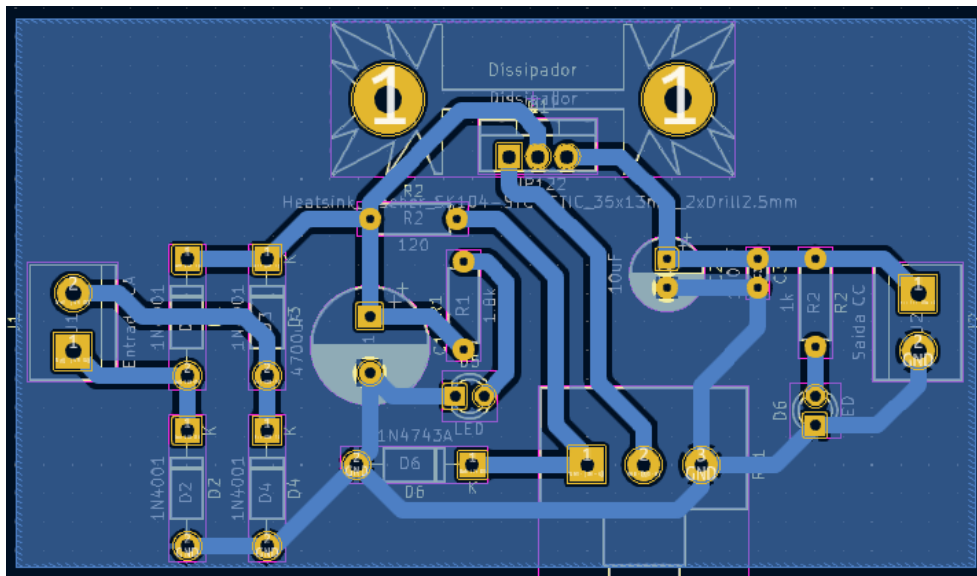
Desenho da placa de circuito impresso da fonte ajustável.
